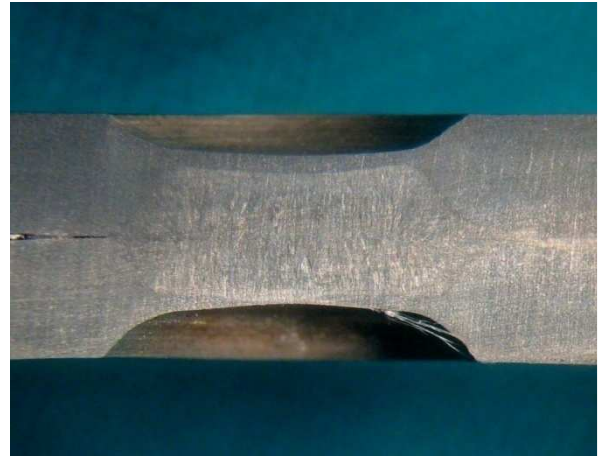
26. Macrografía del punto de soldadura en la probeta de 2.5 mm (10x)
